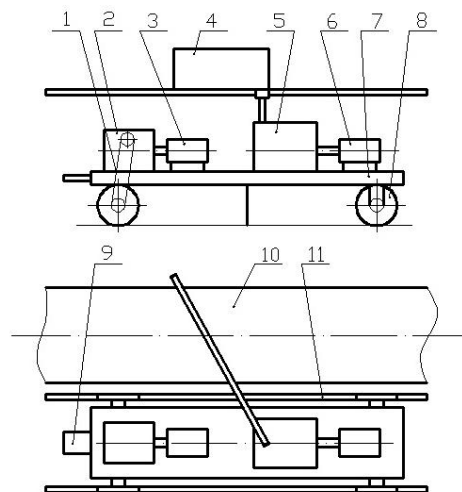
Пересувний пристрій що зіштовхує: 1 – ланцюгова передача; 2 – редуктор; 3 – електродвигун; 4 – плуг; 5 – редуктор; 6 – електродвигун; 7 – конвеєр; 8 – візок; 9 – колесо; 10 – рейка, опора
